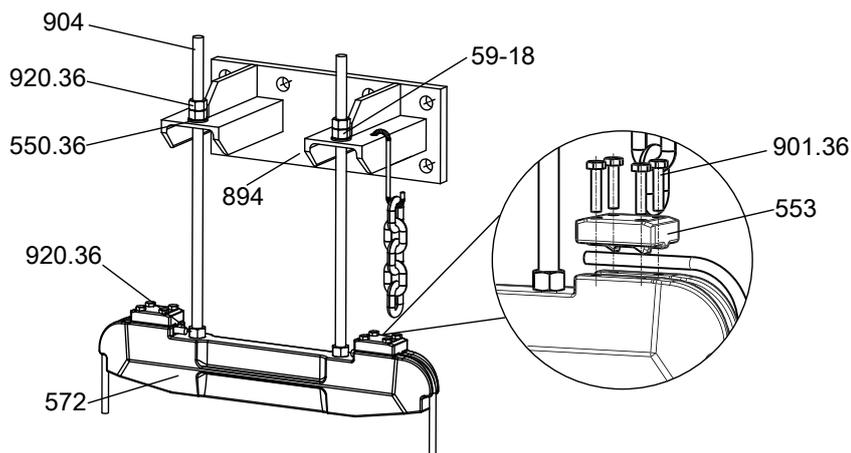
Versiones de consolas para tamaños con diámetro nominal de la boca de impulsión DN 350, DN 400, DN 500, DN 600 y DN 700
